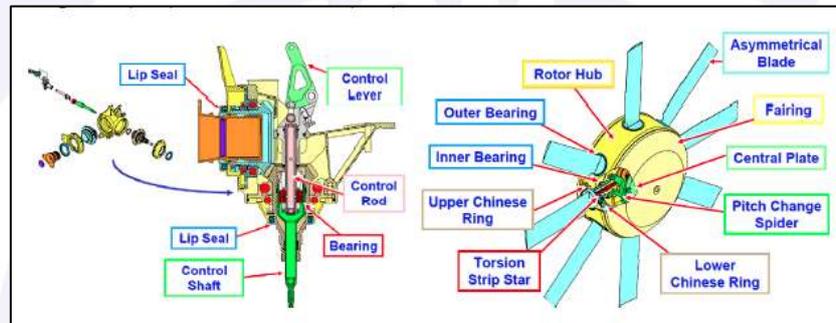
Tail Gear Box (TGB) e Tail Rotor Head (TRH).
